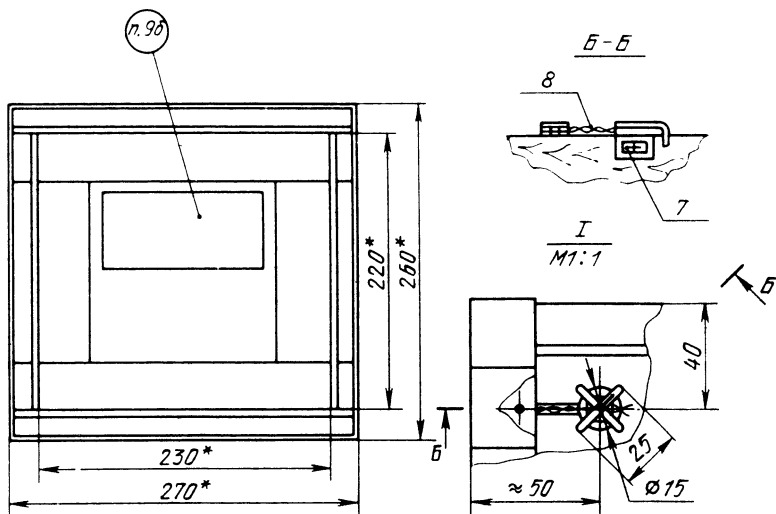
Сборочный чертеж упаковки по варианту Б
